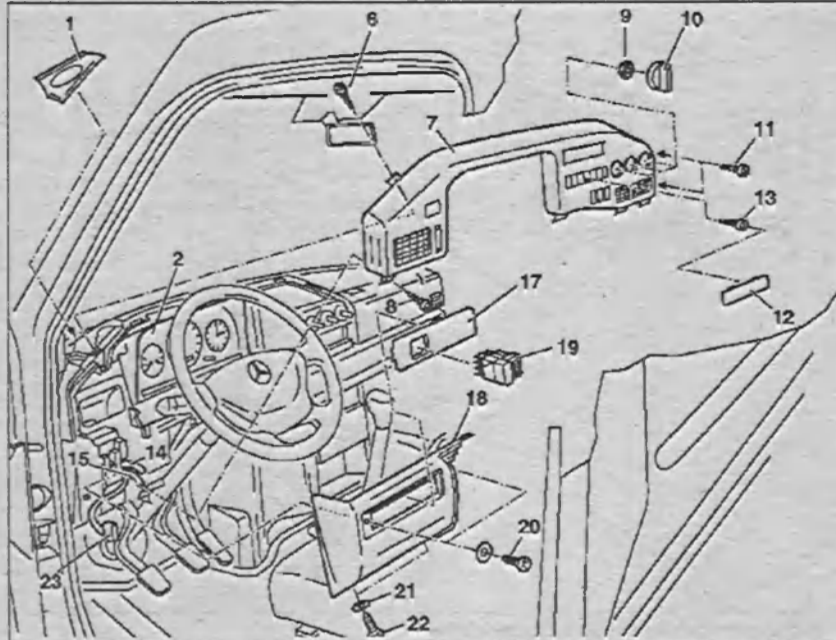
Снятие и установка декоративной накладки щитка приборов:
